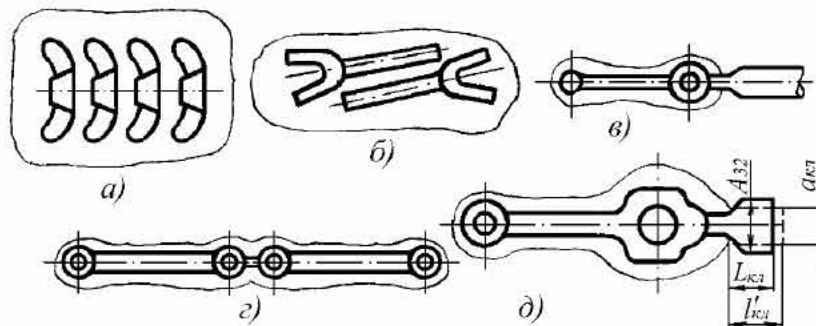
Приклади способів штампування: а), б) – багатоштучне; в) – від прутка; г) – з поворотом заготовки; д) – зі штучної заготовки
